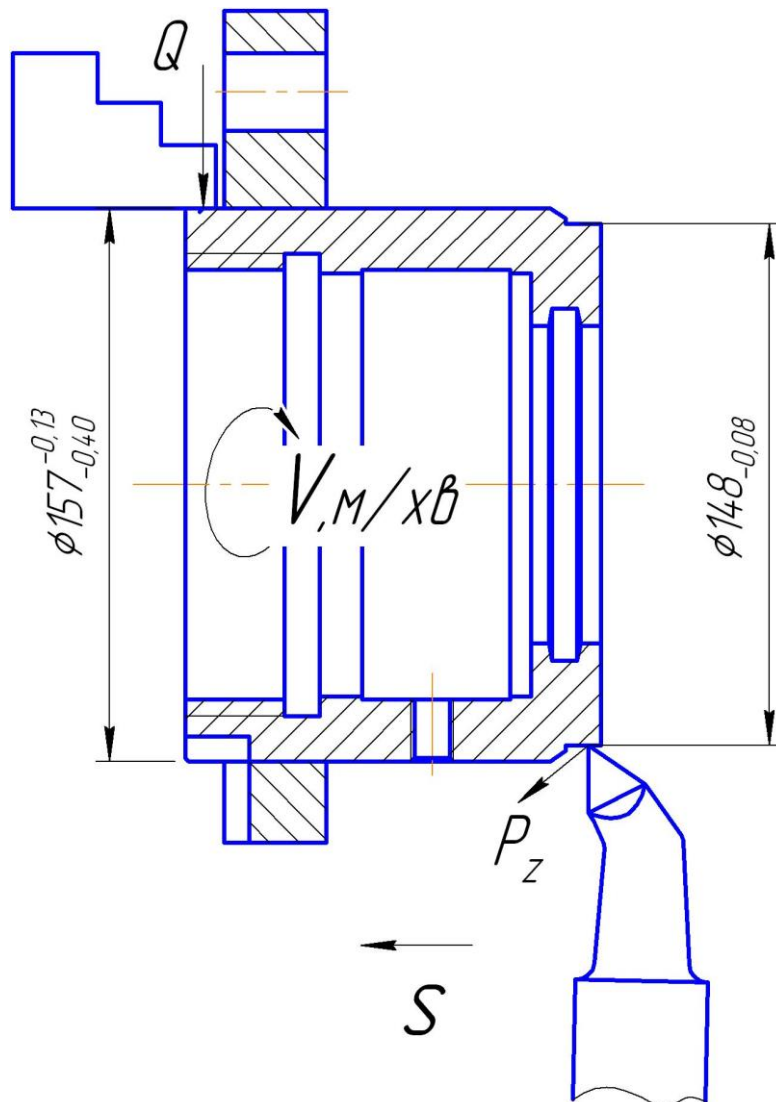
Схема закріплення заготовки в пристрої.
